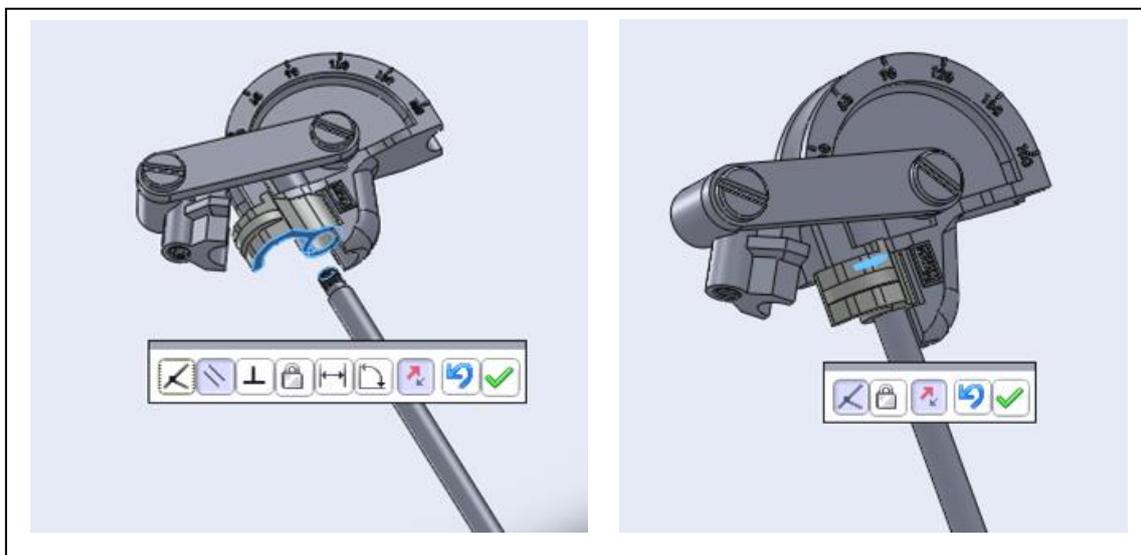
Contraintes parallèle et coaxiale entre l'ensemble précédent et la pièce 2
